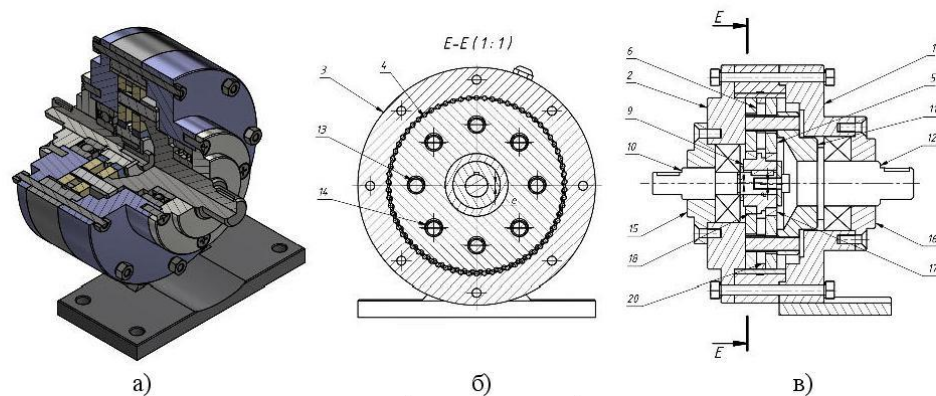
Конструкція планетарно-цівкового редуктора:
